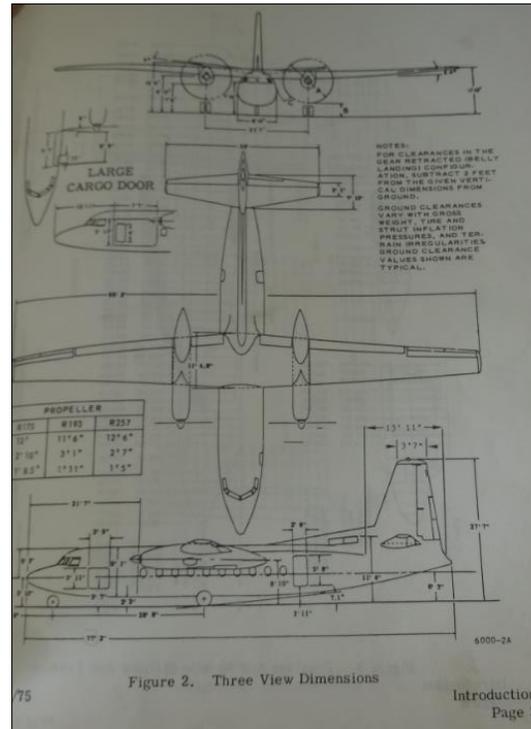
Tres vistas de las Dimensiones del Fairchild F-27
